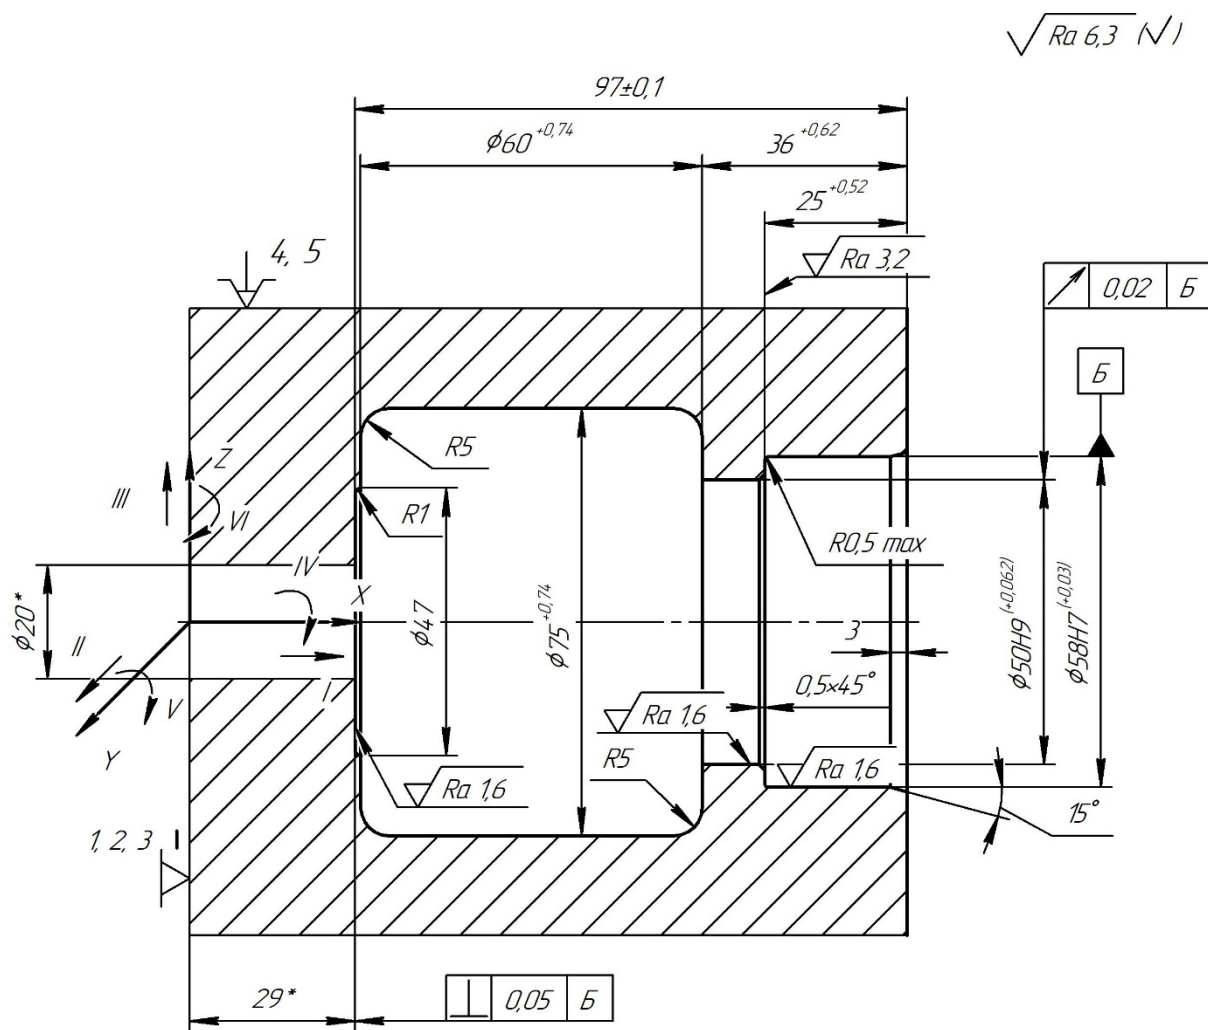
Альтернативна схема базування й закріплення заготовки на операції 030 токарно-гвинторізній
